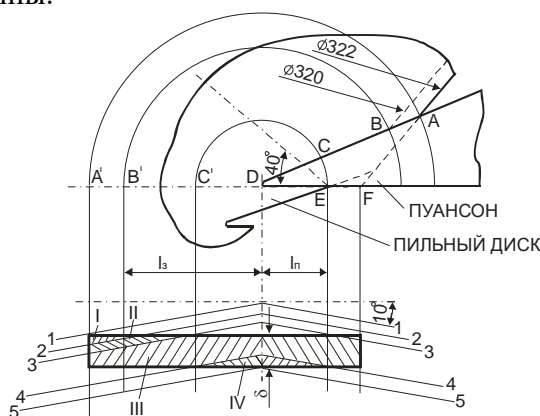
Формообразование и развертка поверхностей зубьев пильного диска при вырубке из листового металла
